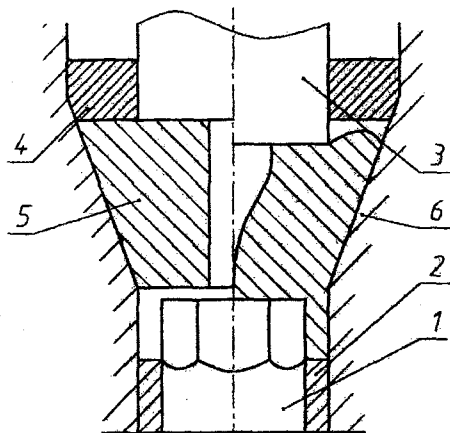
Выдавливание полости сложной формы в заготовке из легированной стали с целью изготовления штампового инструмента (матрицы): 1 – мастер-пуансон; 2 – центрирующая втулка; 3 – толкатель; 4 – центрирующее кольцо; 5 – заготовка; 6 – матрица с конической полостью
